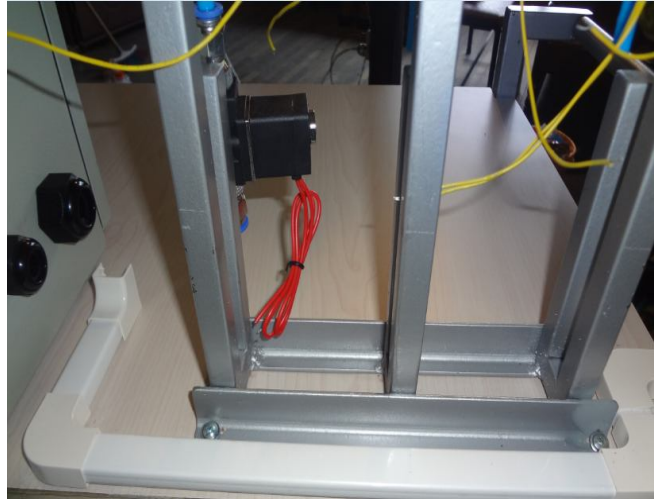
Fijación de soportes para tanques y ruta de cableado (Fuente: Autor)
